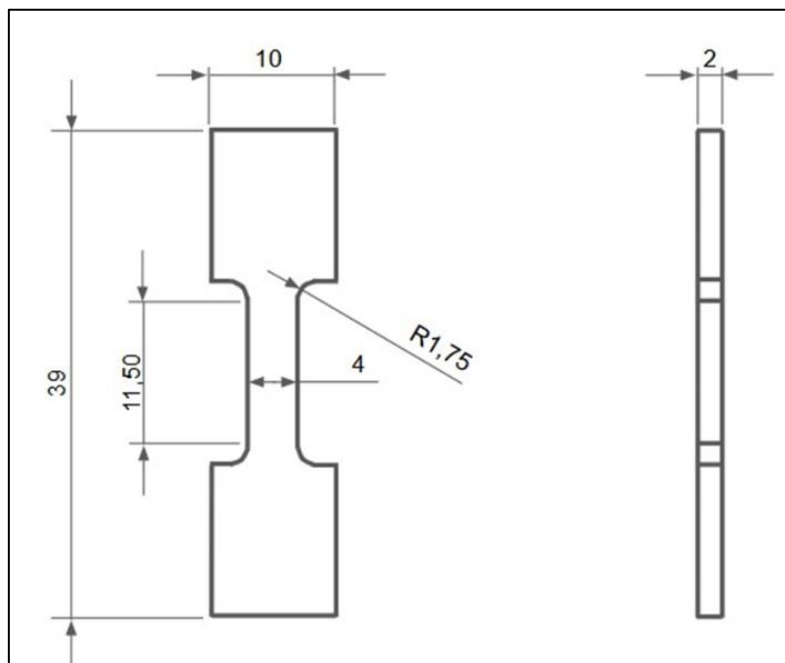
Desenho técnico do corpo-de-prova. Dimensões em milímetros.
